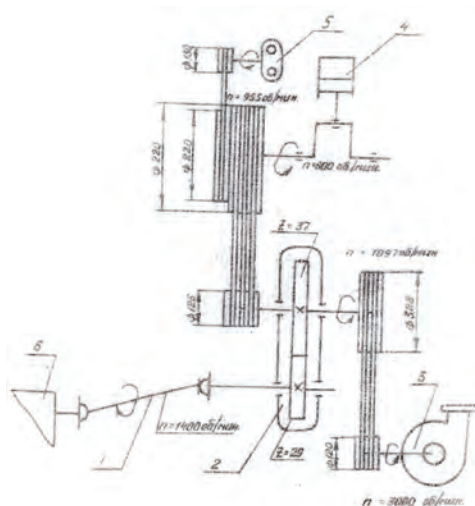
Кинематическая схема установки ППУА - 1600 / 100 на шасси КАМАЗ - 43118 - 1016 - 15
